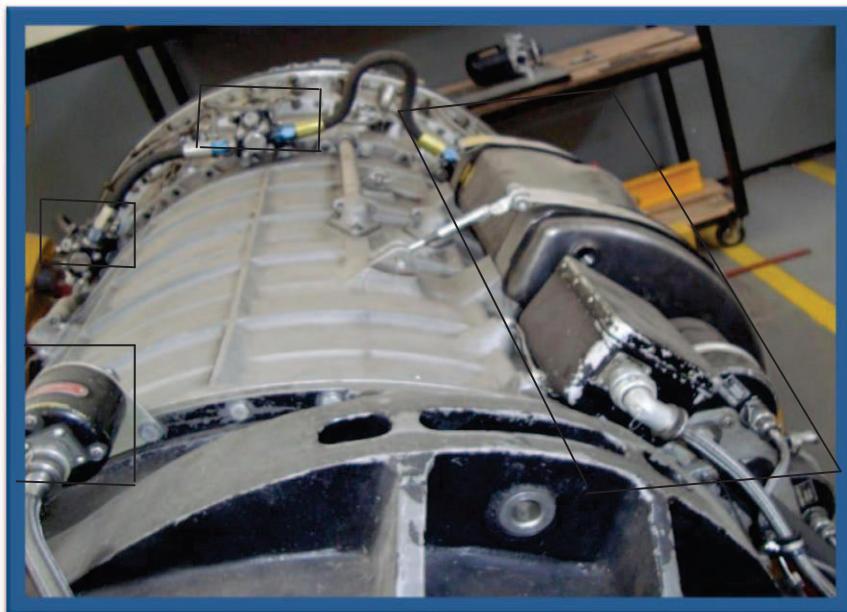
Accesorios marcados que se retiraran del motor J-65
